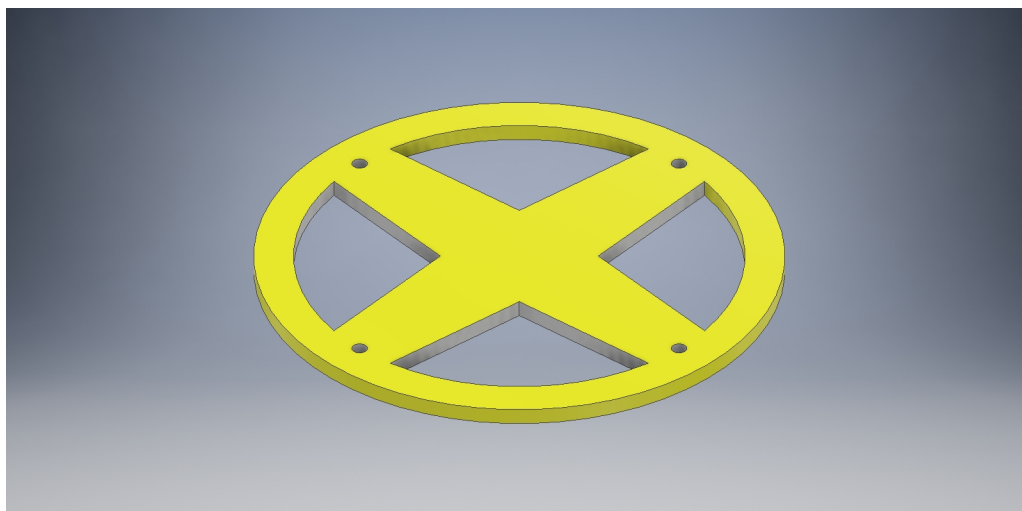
Soporte inferior para la placa principal del diseño mecánico del dispositivo esclavo
